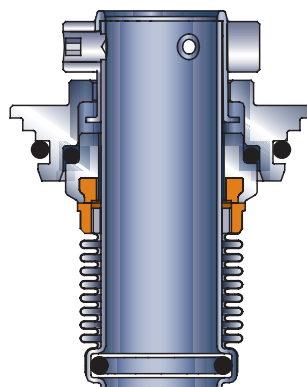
Картриджевый металлический сальфонный уплотнитель
